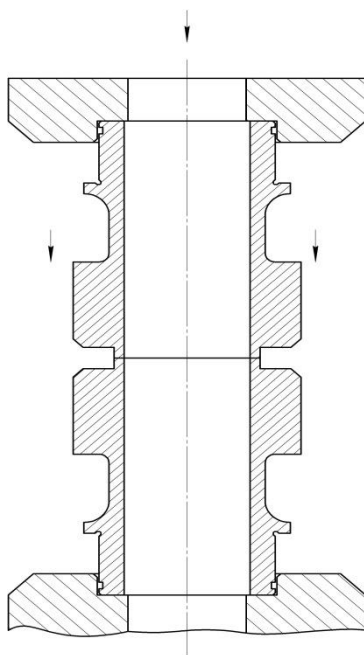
Заготовки с указанием мест приложенных усилий
